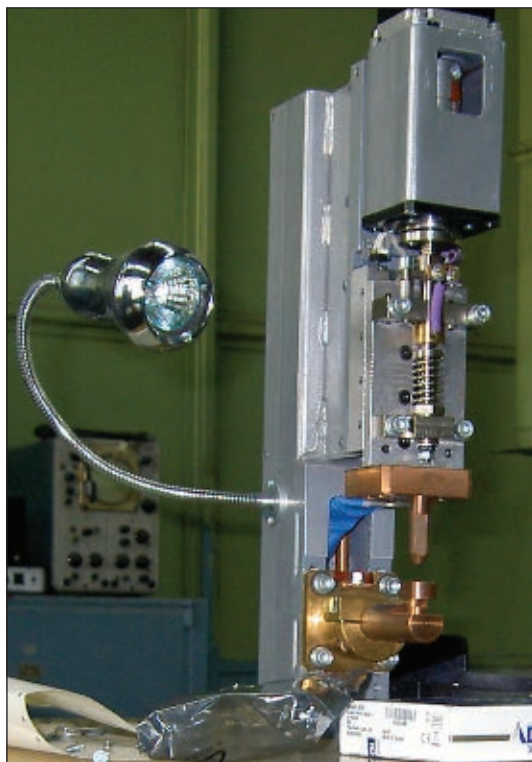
Сварочная головка машины МТЧ-5.05
